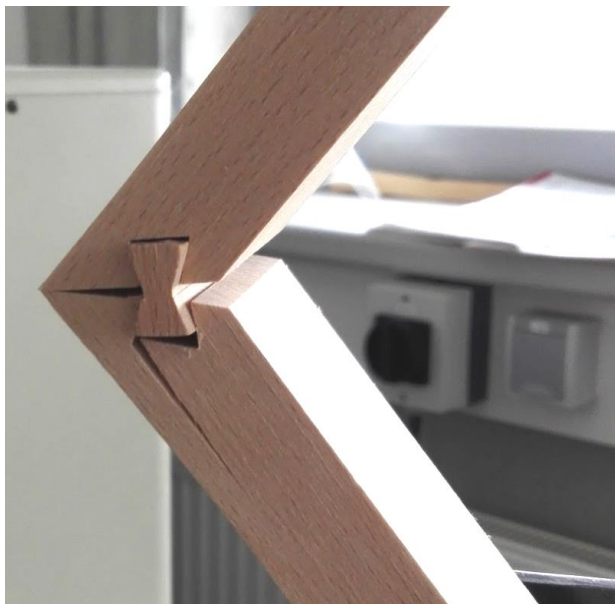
Vytvoření drážky pro spojky pomocí frézky
